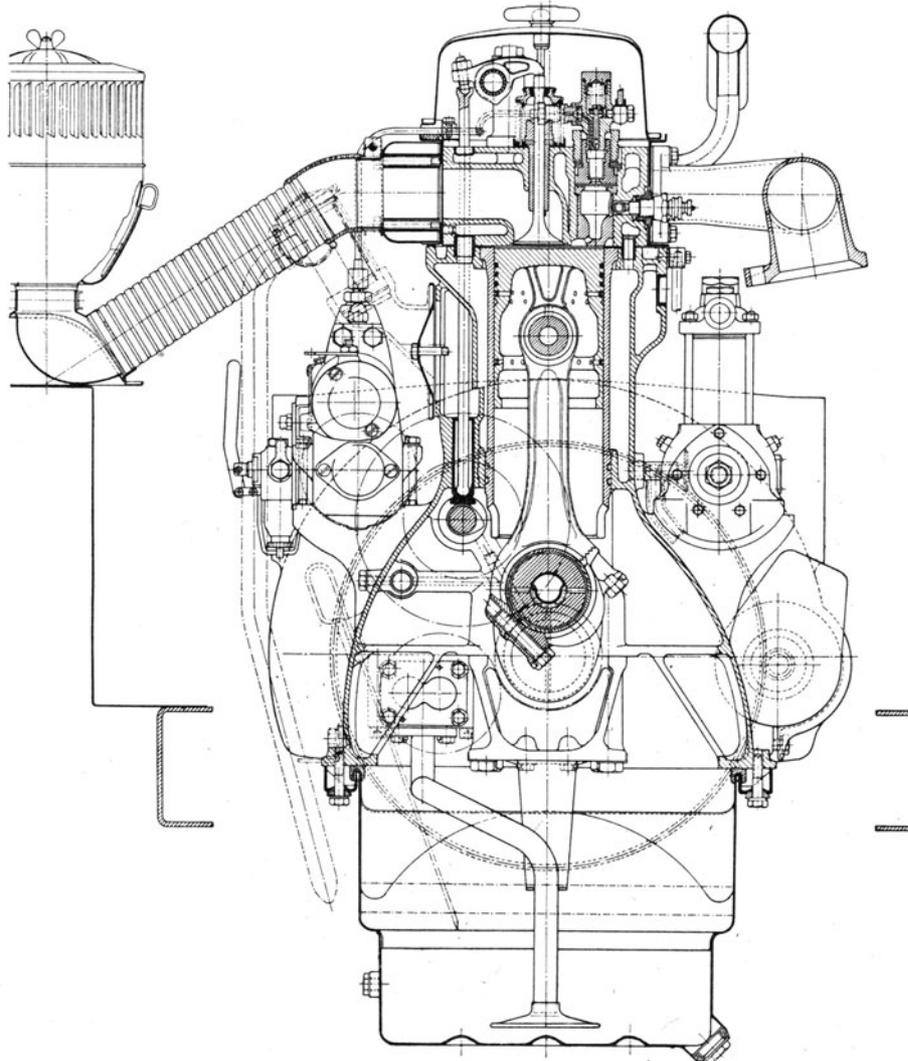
Fahrzeugdieselmotor F 4 M 513 der Klockner-Humboldt-Deutz A G
